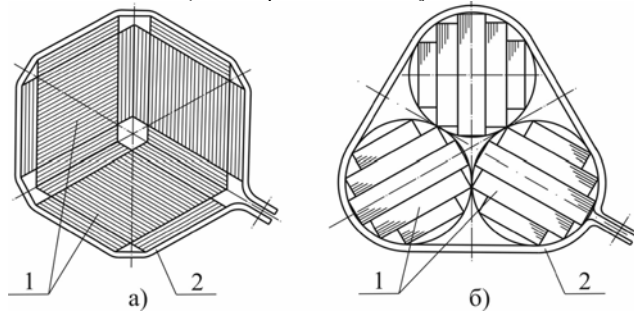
Сборка для обработки торцевых поверхностей стержней пространственных магнитных систем с параллельными (а) и цилиндрическими (б) образующими поверхностями: 1 – стержень; 2 – крепежное приспособление (хомут)
